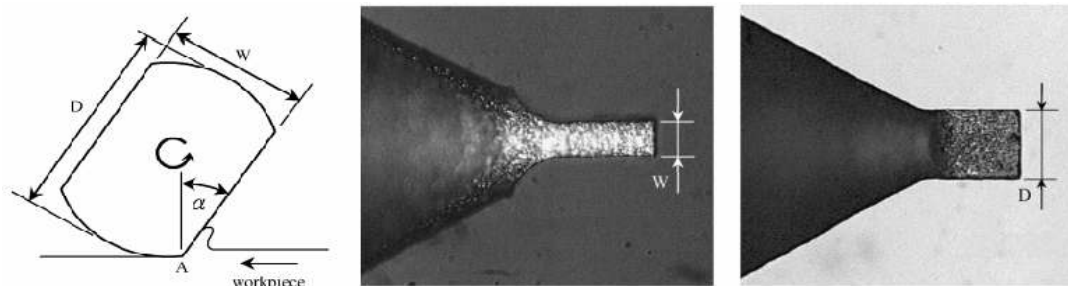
, Seitenansicht eines Mikrowerkzeuges [Cher06]
